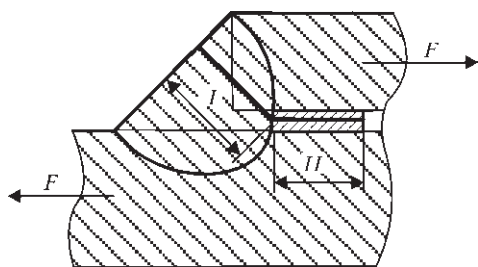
Схема расчетного сечения сварно-паяного соединения внахлест
